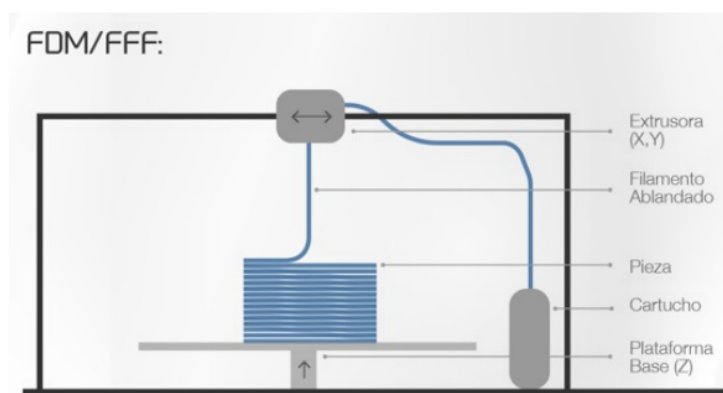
Partes de una impresora 3D de la tecnología DFM. [27]
